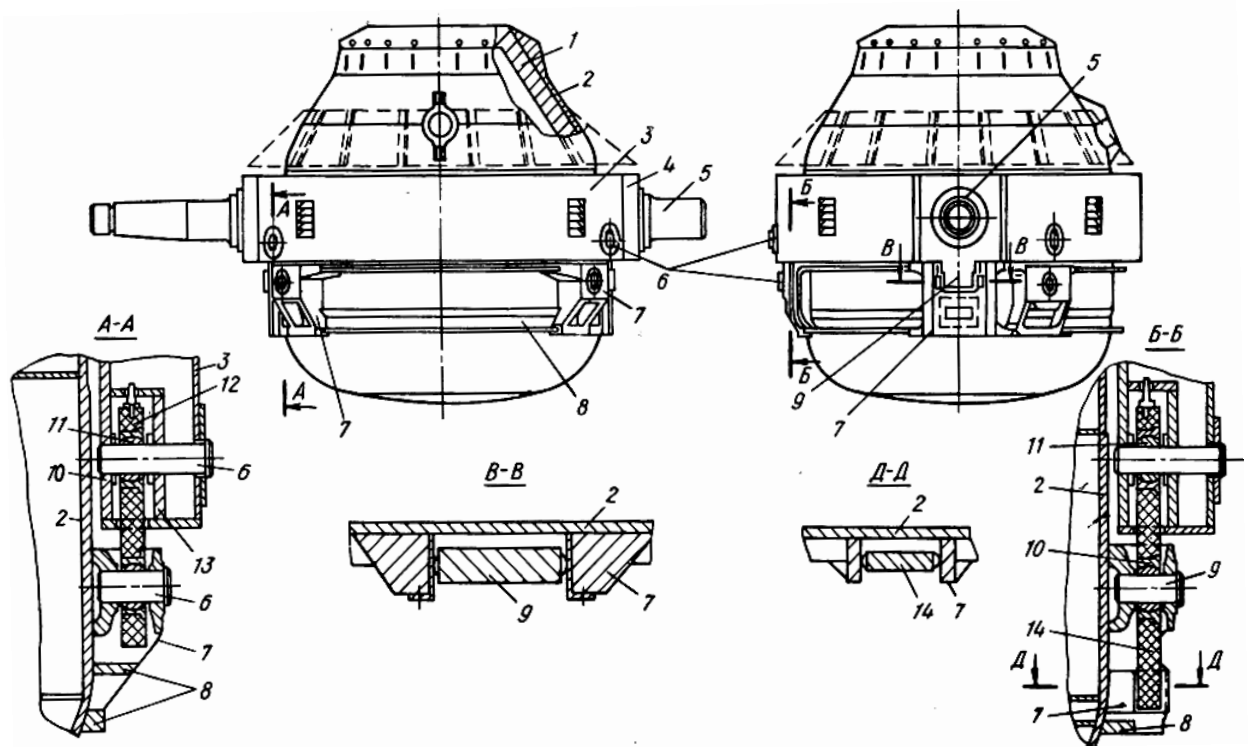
Крепление корпуса в опорном кольце с помощью тяг.
